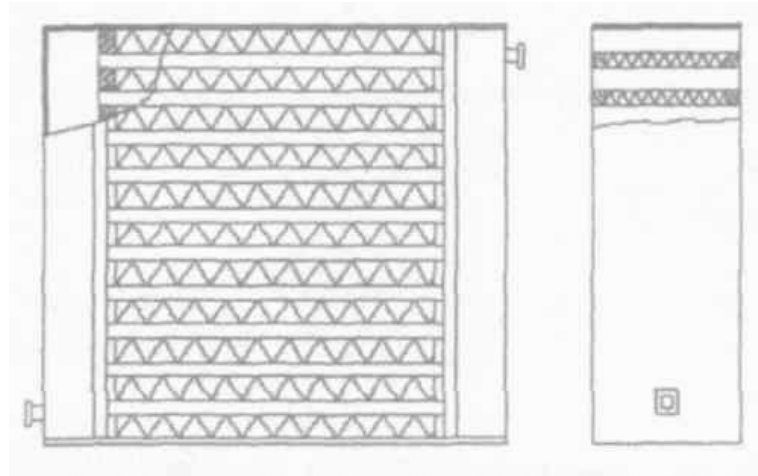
Схема ПРТ із привареними колекторами
